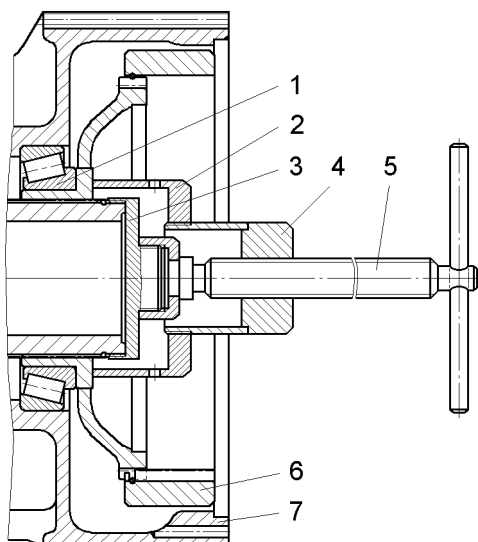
Запрессовка кожуха планетарной передачи:
